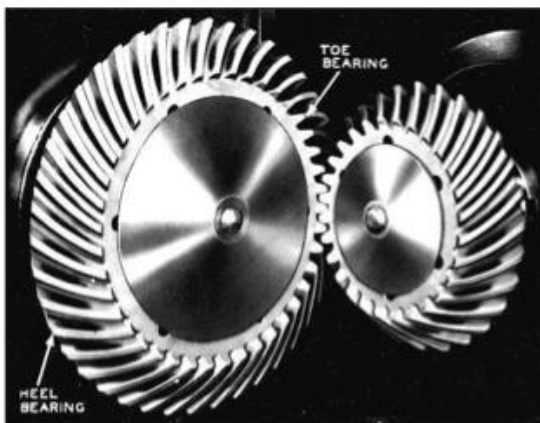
Pormenor do encaixe dos dentes de uma engrenagem
